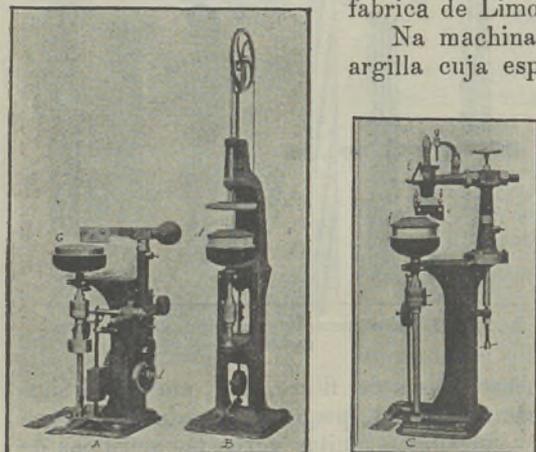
Jogo de machinas Faure, para moldação de pratos
